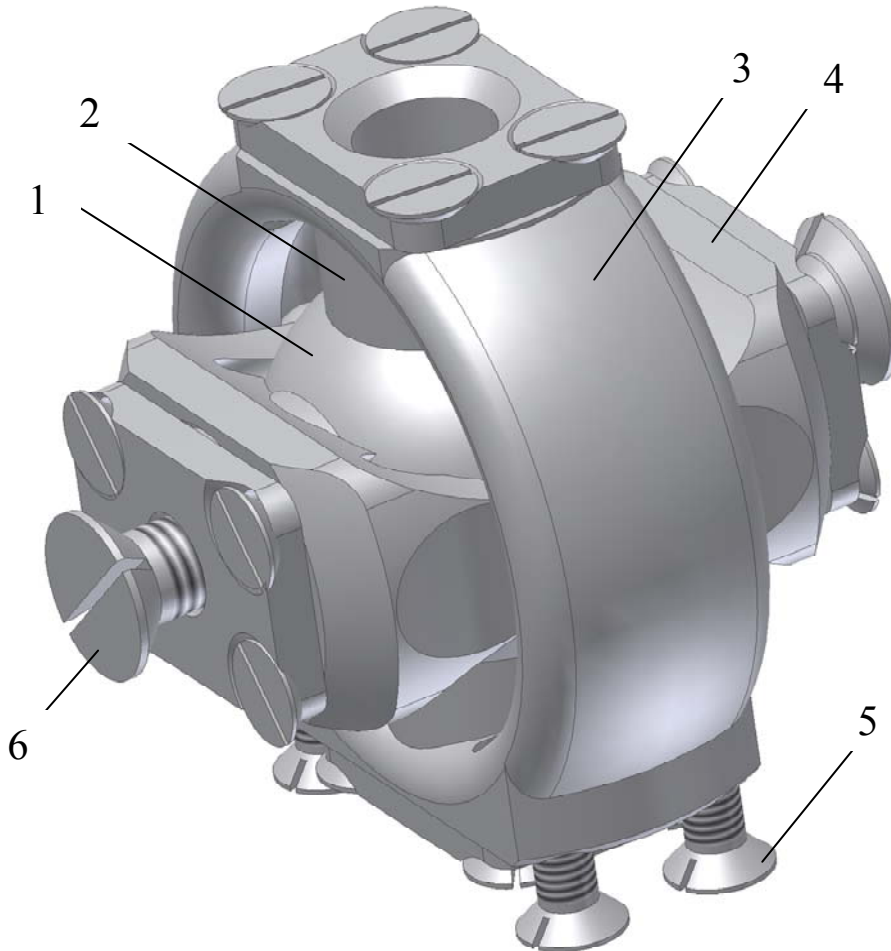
Розроблена прецизійна сферична опора ковзання (із кожухом)
